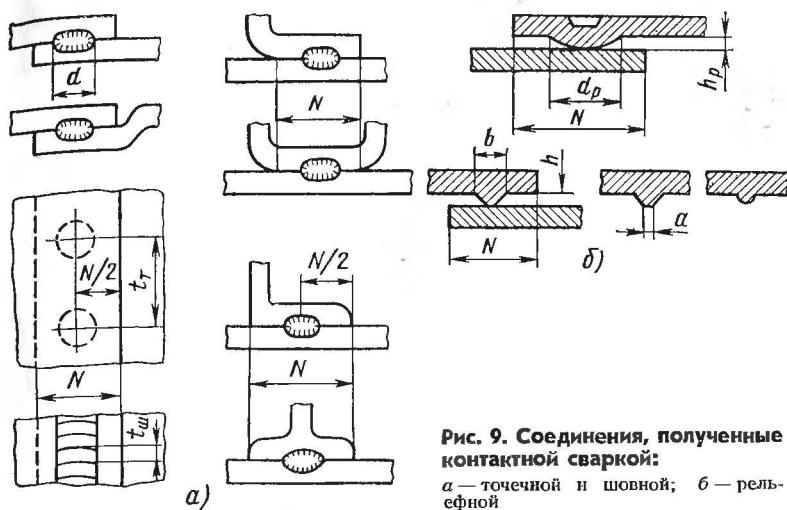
Соединения, полученные контактной сваркой:
